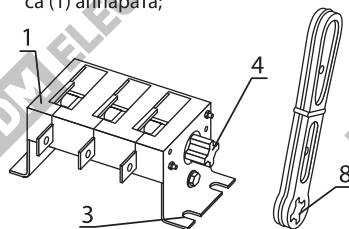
Выключатель-разъединитель ВР32 с боковой рукояткой
